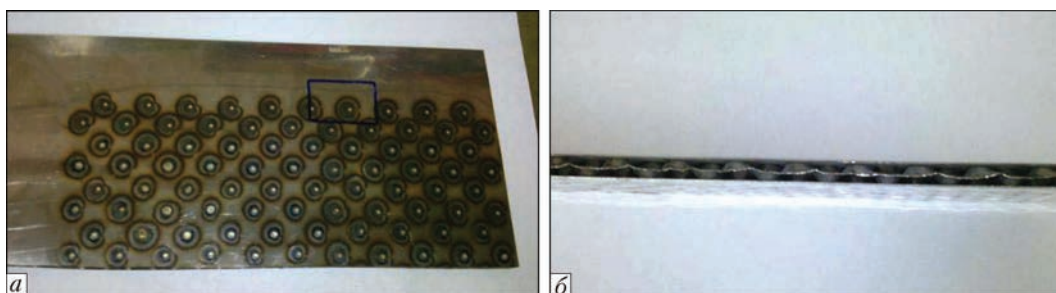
Изображение трехслойного образца с двойной точечной сваркой: *а* – вид сверху; *б* – вид с торца
